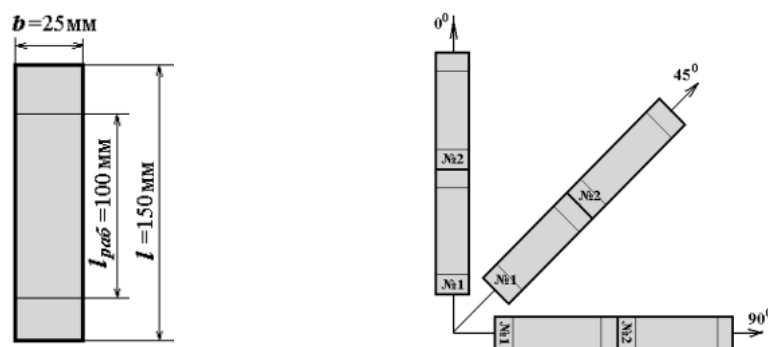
Форма, размеры и схема раскроя образцов
